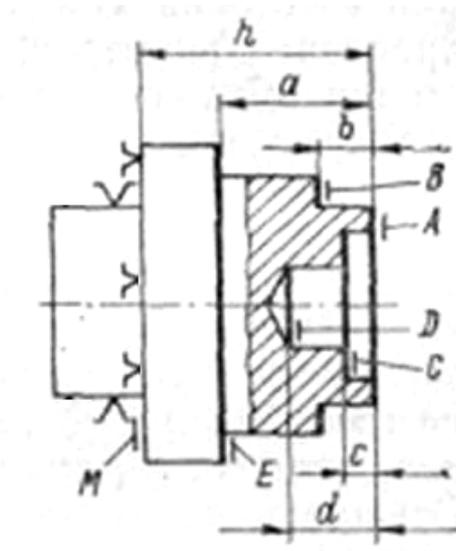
Использование настроечной базы А при обработке заготовки на револьверном станке
